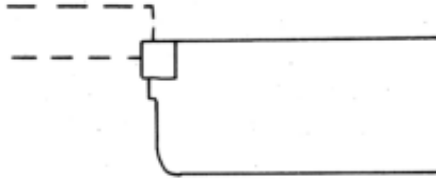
Кант с боковой стороны и со стороны скользящей поверхности
